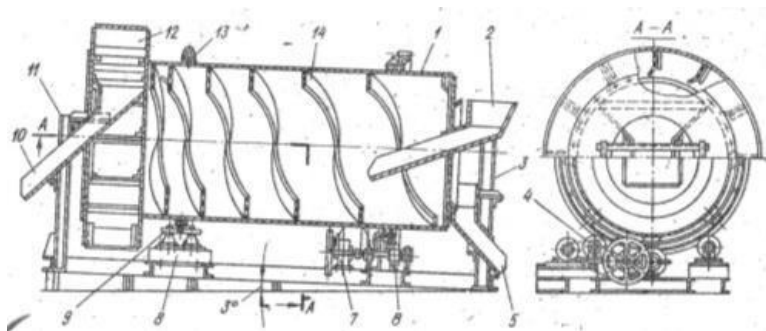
Спиральный барабанный сепаратор типа СБС: 1 – барабан; 2, 3 – загрузочный желоб и стойка его крепления; 4 – опорный ролик; 5 – желоб всплывшего продукта; 6 – привод барабана; 7 – редуктор привода; 8 – рама; 9 – упор-
